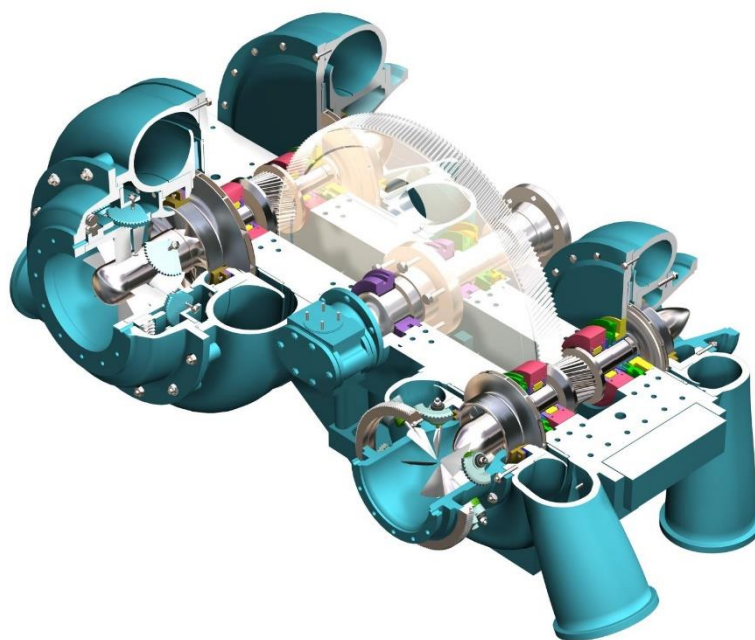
а. Двухвальный четырехступенчатый центробежный компрессор ОАО «Дальэнергомаш» для подачи воздуха в пневматические системы (корпуса ступеней и верхняя крышка корпуса повышающей зубчатой передачи сняты для наглядности)
